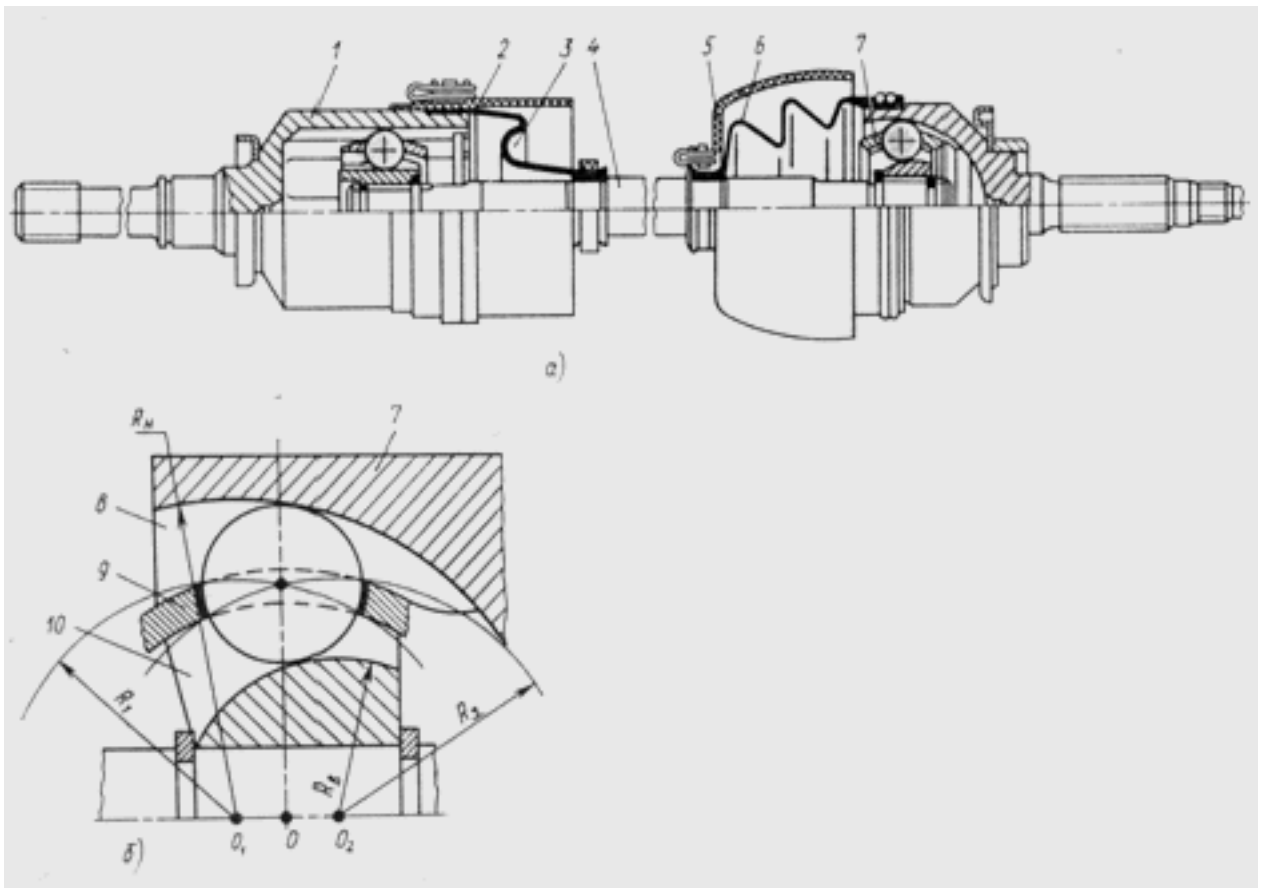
Привод переднего колеса автомобиля «ВАЗ»–2121, «Нива»: а – конструкция; б – схема наружного шарнира. 1,7 – внутренний и наружный шарнир, 2,5 – защитные чехлы, 3,6 – защитный кожух, 4 – вал.
